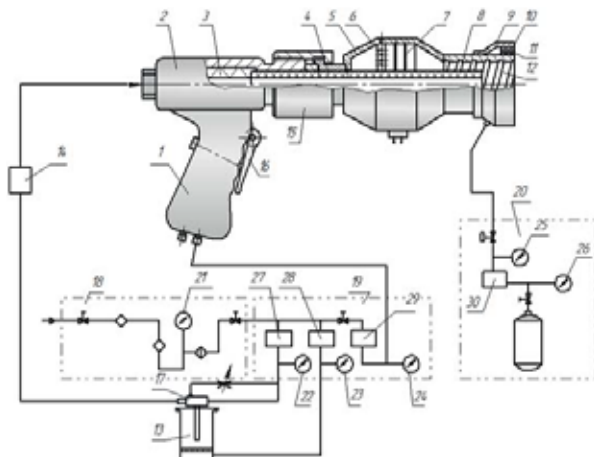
Устройство для нанесения покрытий из полимерных порошковых композиций электрогазопламенным способом: 1 – рукоятка; 2 – зарядный элемент; 3 – ствол; 4 – керамическая трубка; 5 – корпус узла нагрева; 6 – тороидальный коллектор; 7 – проволочные нагреватели; 8 – выходной насадок; 9 – корпус инфракрасного излучателя; 10 – керамическое кольцо инфракрасного излучателя; 11 – отверстия в керамическом кольце; 12 – винтообразные канавки; 13 – порошковый питатель; 14 – узел предварительного нагрева; 15 – муфта присоединительная; 16 – курок; 17 – эжекторный насос; 18 – блок подготовки воздуха; 19 – пневматическая панель; 20 – газовый блок; 21, 22, 23, 24 – манометры; 27, 28, 29, 30 – регуляторы давления.
